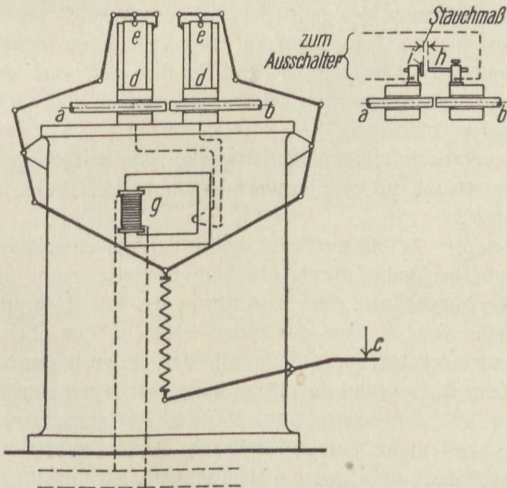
Schema einer Stumpfschweißmaschine.
